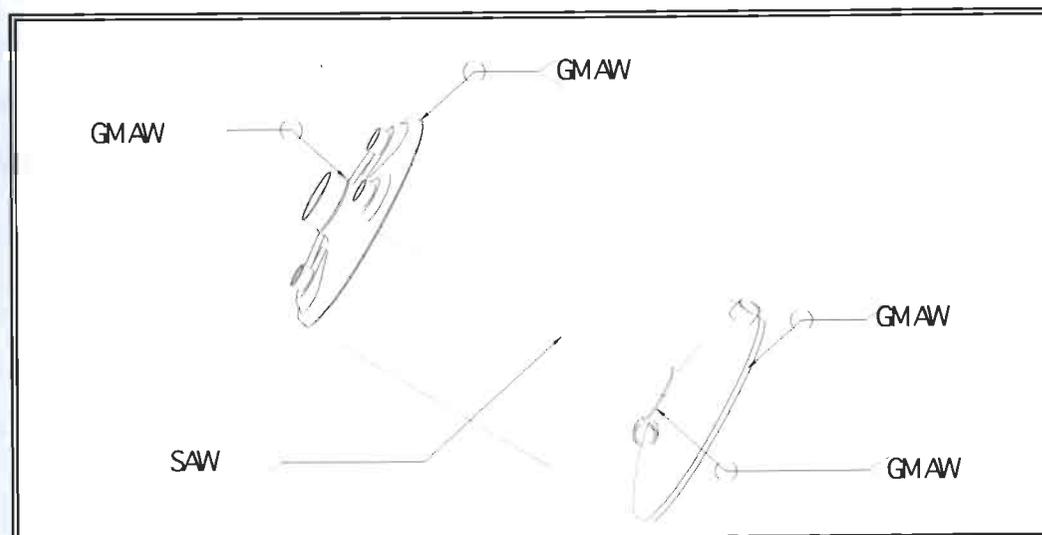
Partes soldadas por el proceso GMAW y SAW en el recipiente del calentador de agua
